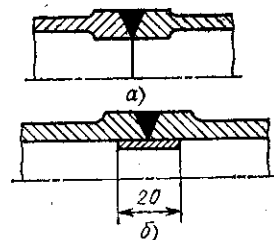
Предотвращение проплава при сварке:
